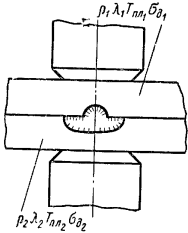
Точечная сварка разнородных металлов [1]
